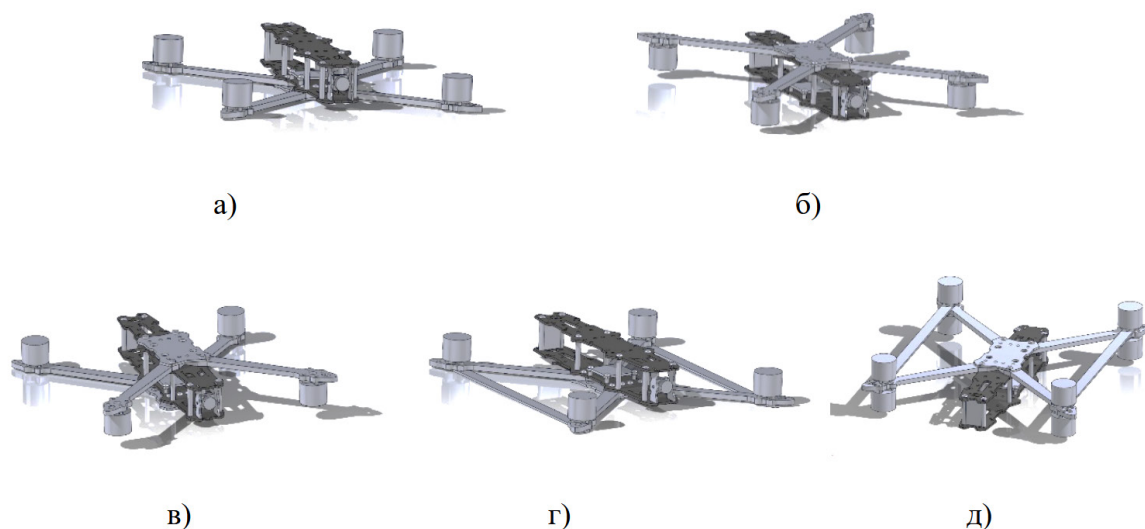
Модели летательных мобильных роботов: а) 4 двигателя над корпусом; б) 4 двигателя под корпусом; в) 2 двигателя впереди над корпусом и 2 сзади двигателя под корпусом; г) 4 двигателя над корпусом с усиленным корпусом; д) 8 двигателей – 4 над корпусом и 4 под корпусом с усиленным корпусом
